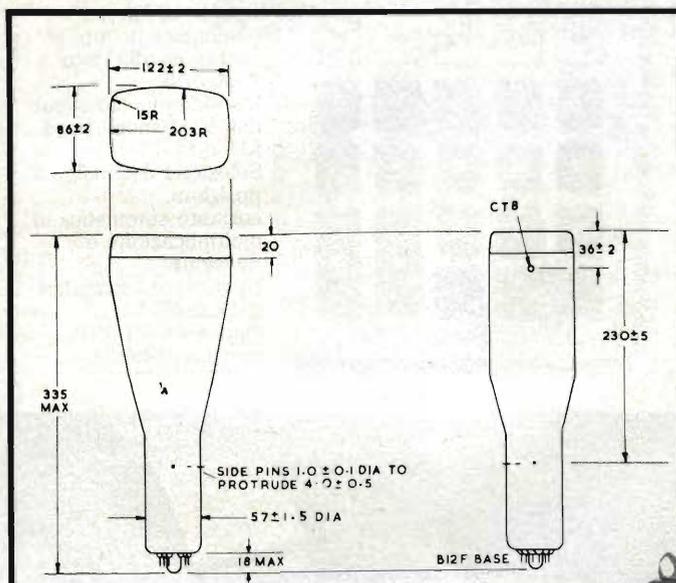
Tubo catodico per oscilloscopio. Il complesso di elettrodi detto "cannone elettronico" è compreso nella parte inferiore, più sottile e vicina ai terminali.
